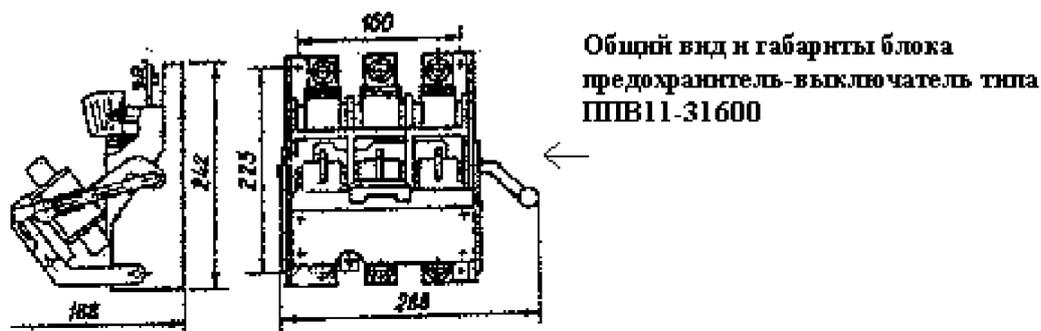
Общий вид и габариты блоков предохранитель-выключатель
